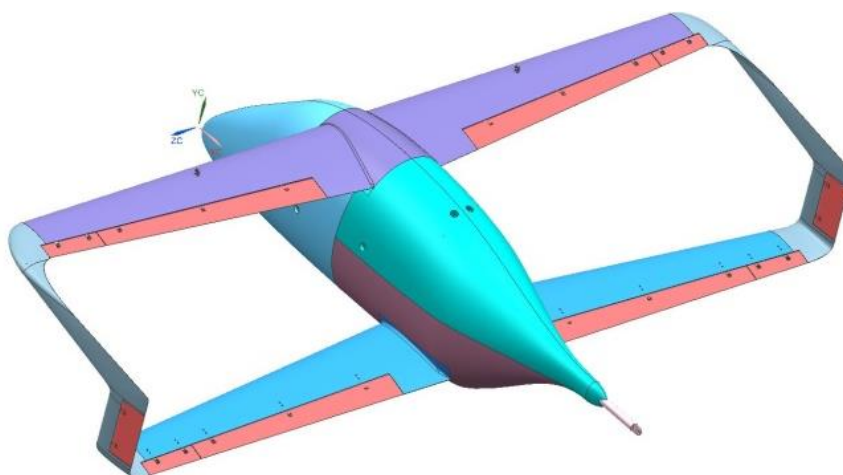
Общий вид продувочной модели самолета с крылом коробчатой схемы
